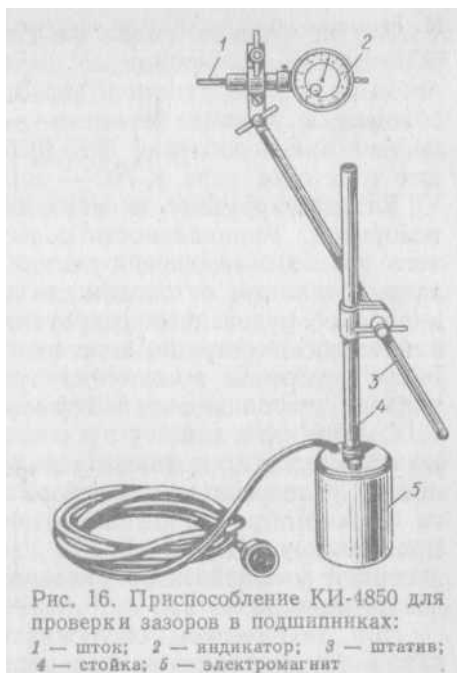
Приспособление КИ-4850 для проверки зазоров в подшипниках:
